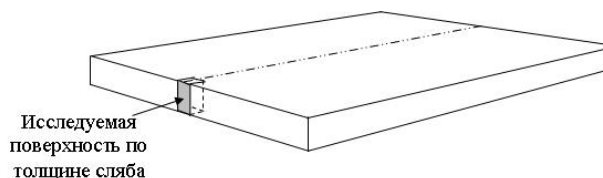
Схема отбора темплетов из слябовой непрерывнолитой заготовки
